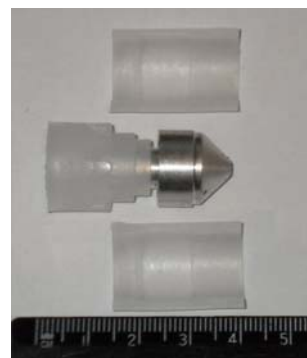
Вид метаемой сборки, для установки калибром 18мм.
